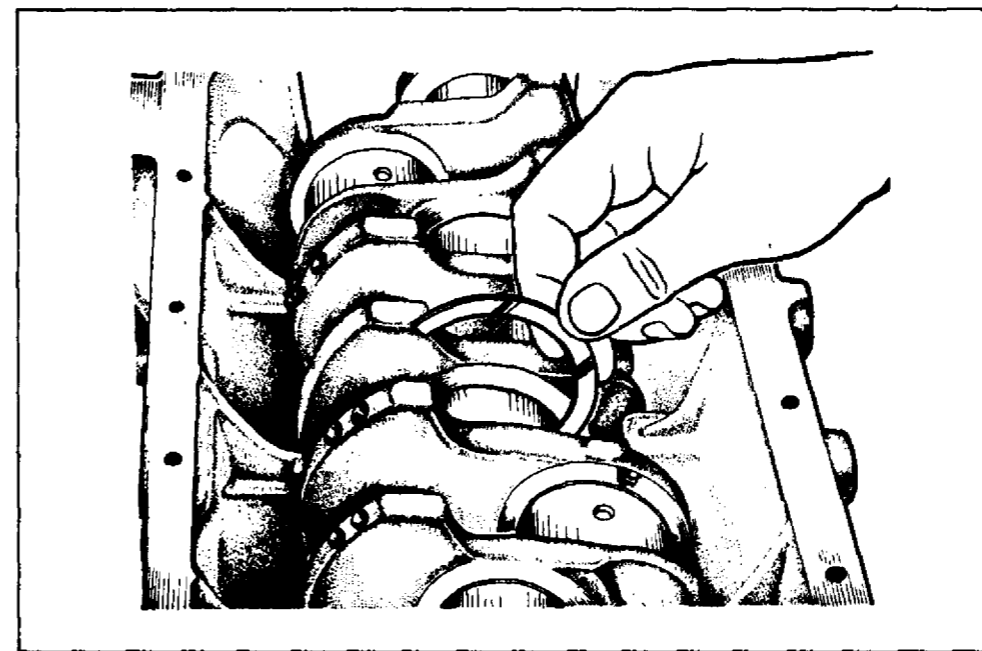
Установка упорных полуколец коленчатого вала в гнездо среднего коренного подшипника
